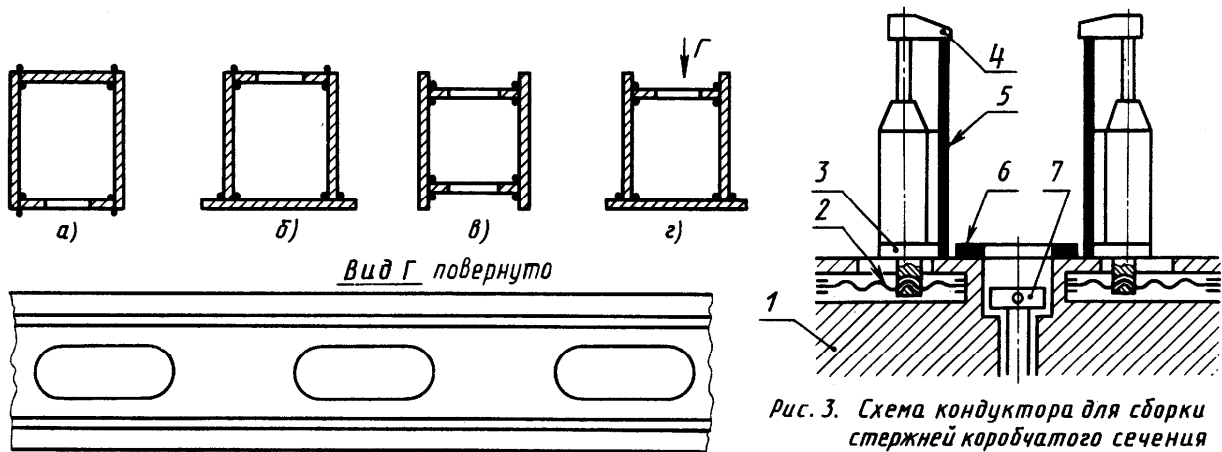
Схема кондуктора для сборки стержней коробчатого сечения
